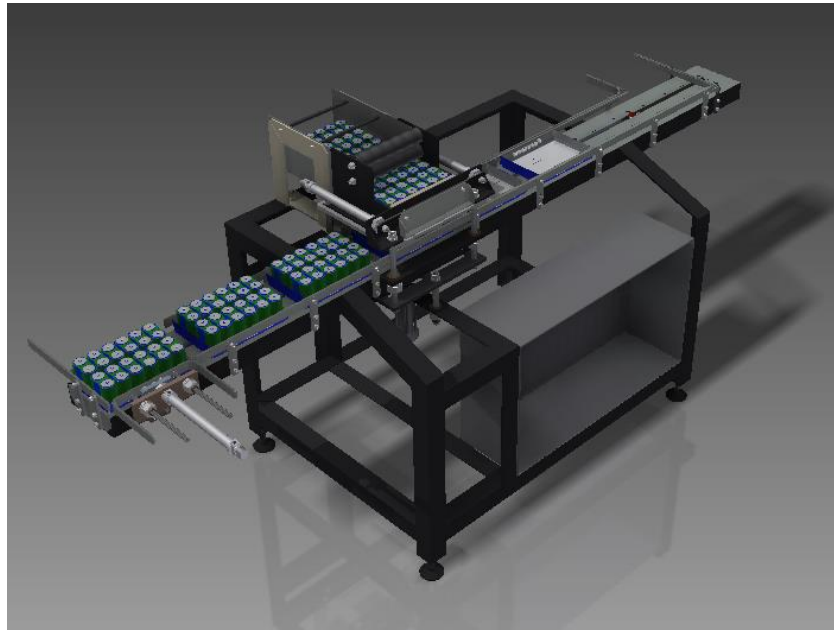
Vista en CAD de la máquina Llenadora de Bandejas completa
